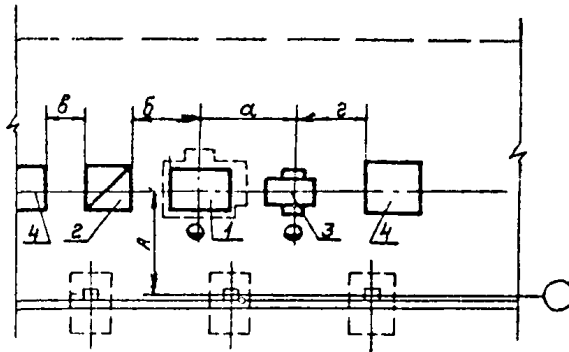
Схема расположения штамповочных линий на базе винтовых прессов с дугостаторным приводом:
